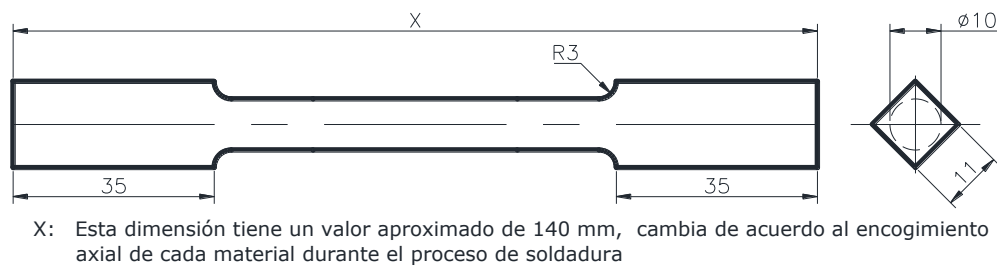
Dimensiones de la probeta para el ensayo de torsión
